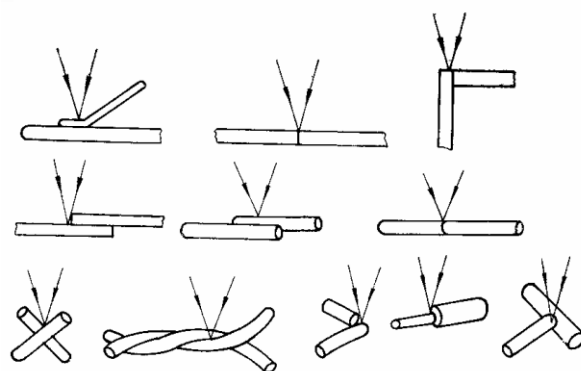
Типы соединений, выполняемых точечной сваркой
